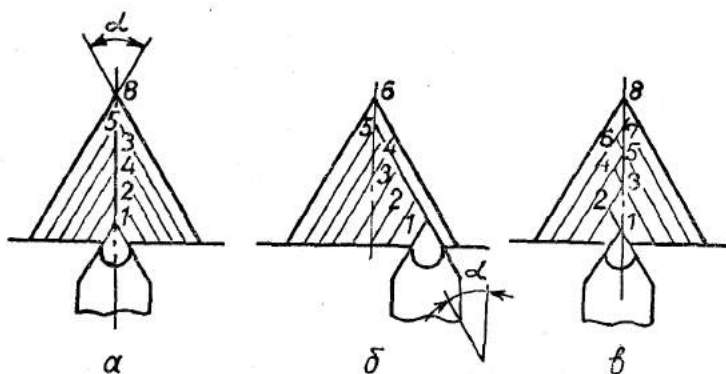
Схеми багатопрохідної обробки різцями: 1—8 — точки позиціонування різця.
